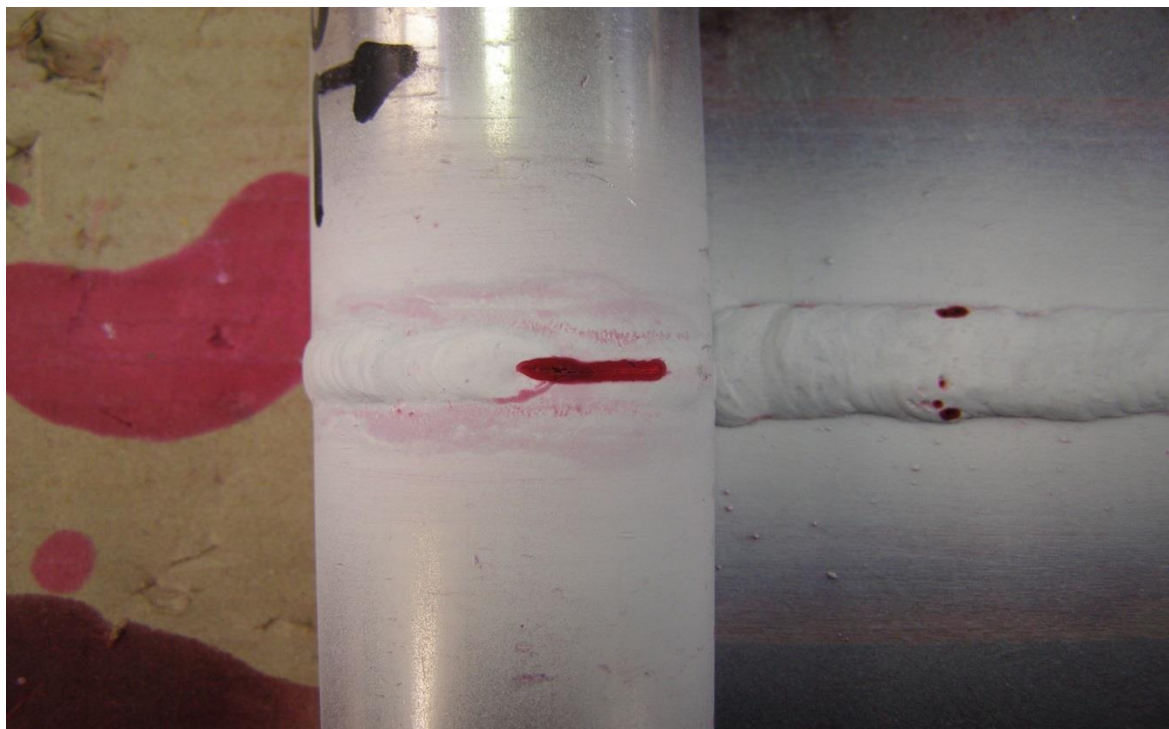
Očištění povrchu zkušební vzorku od penetrantu, ihned po uplynutí penetračního času
